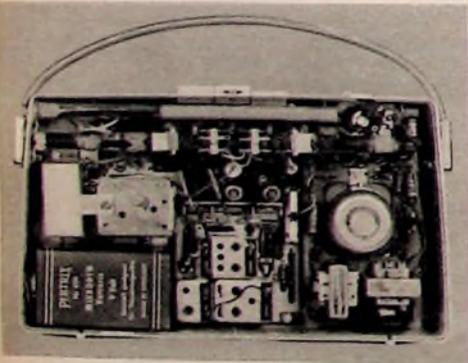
(oben). Innenansicht des „Kavalier 3291“
